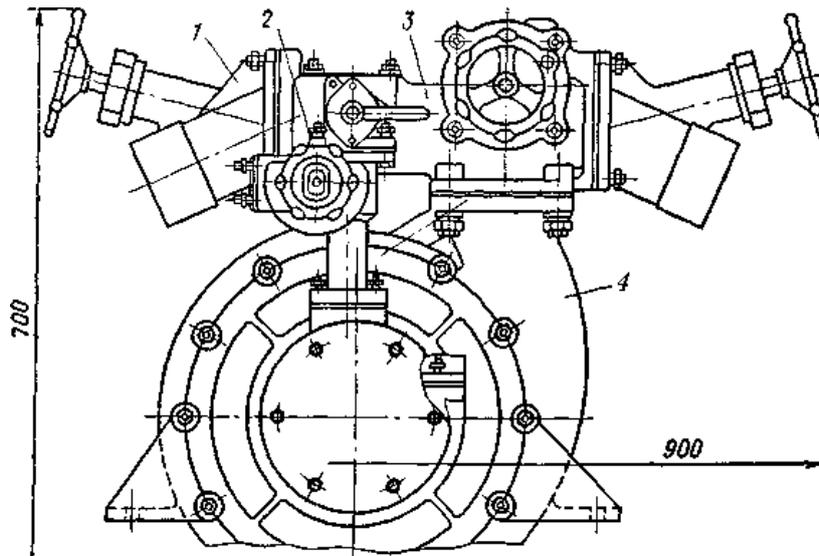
Общий вид пожарного насоса ПН-40УА: 1 – задвижка; 2 – пеноноситель; 3 – напорный коллектор; 4 – корпус насоса
